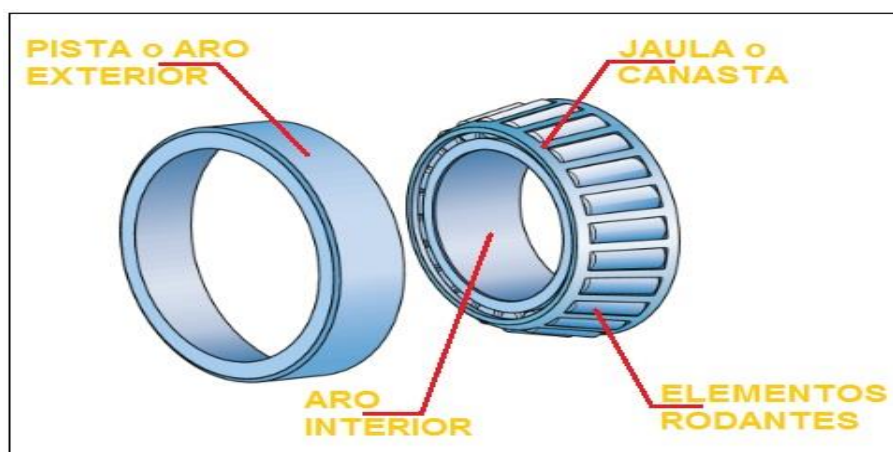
Partes de un rodamiento cónico. Elaborado por: Robinson Tapia
